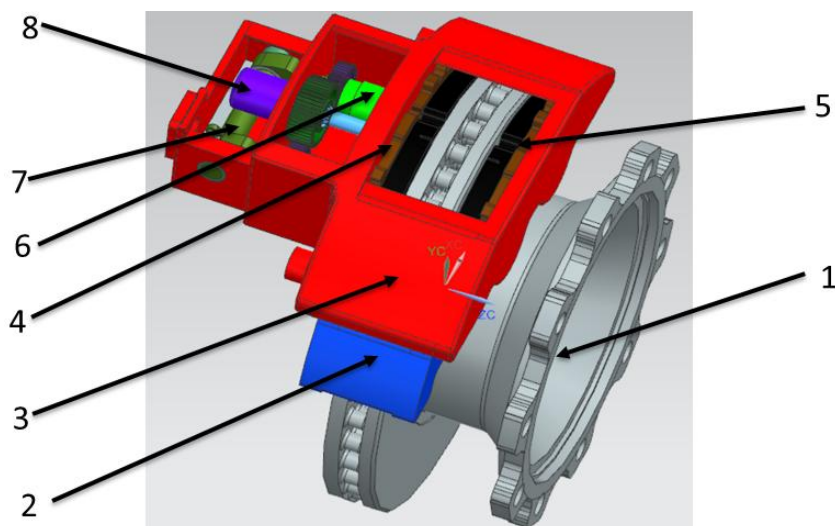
Дисково-колодочное тормозное устройство с электромеханическим регулятором тормозного момента: 1 – диск; 2 – скоба; 3 – суппорт; 4 – внутренняя колодка; 5 – внешняя колодка; 6 – прижимающий элемент; 7 – кулачок пневматического привода; 8 – электродвигатель регулирования тормозного момента
